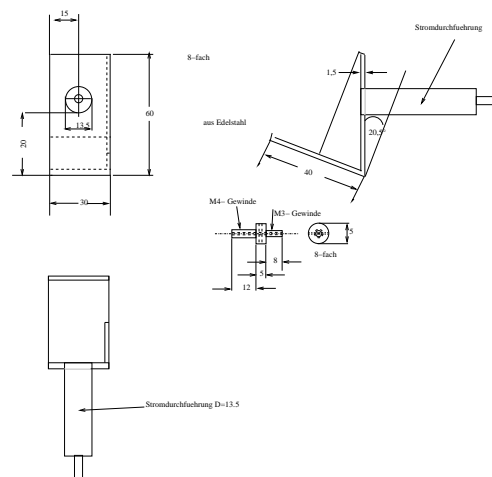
Technische Zeichnung der Trichterelektroden G2.. Die Elektrode G2' ist baugleich.
